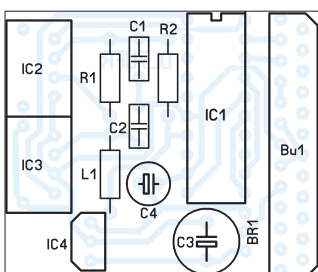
Bestückung des Wandler für die RS232-Schnittstelle
